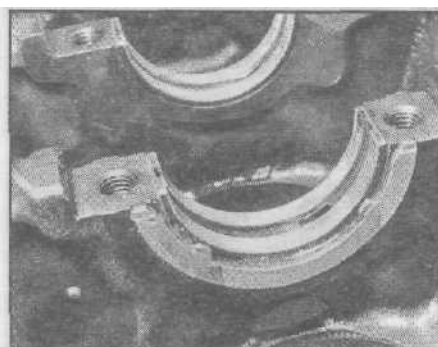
Расположение упорных полуколец на центральном подшипнике
